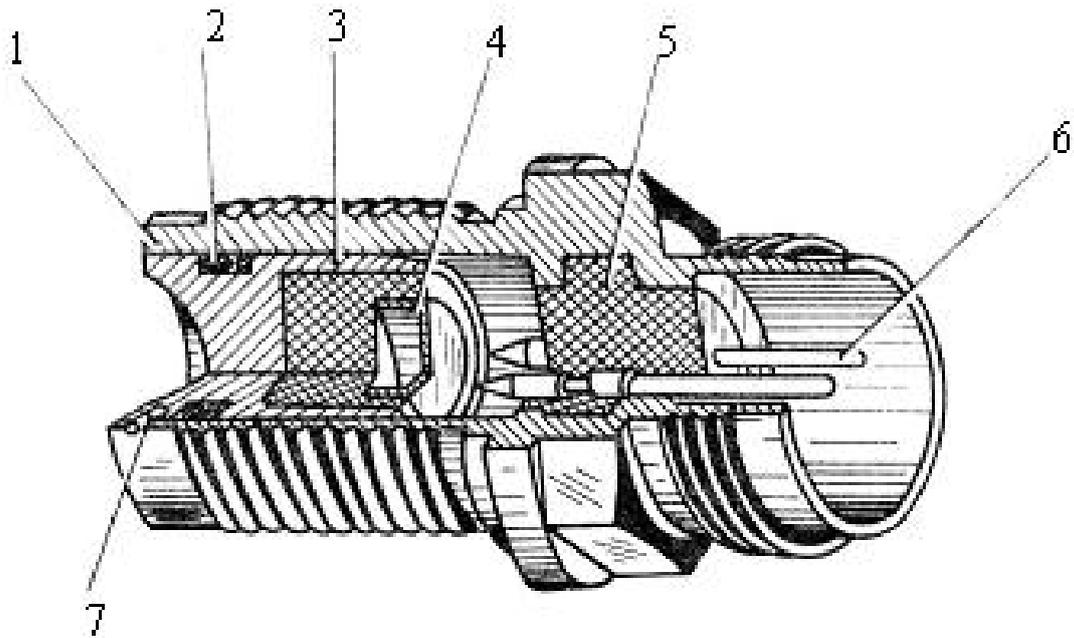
Сигнализатор давления: 1 – корпус; 2 – кольцо; 3 – поршень; 4 – доньшко; 5 – изолятор; 6 – контакт; 7 – штифт
